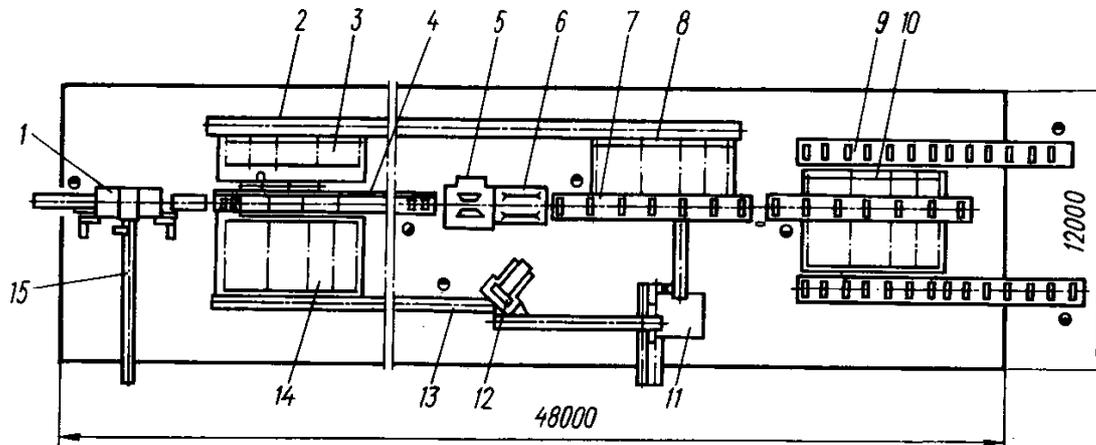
Технологическая схема лесопильного цеха с головным фрезерно-брусующим станком для тонкомерного сырья: 1 – окорочный станок; 2, 13 – ленточные конвейеры; 3, 8, 14 – цепные конвейеры; 4, 5, 7 – фрезерно-брусующий станок с околостаночной механизацией; 6 – делительный модуль; 9 – роликовый конвейер; 10 – реверсивный цепной транспортер; 11 – устройство для сортировки щепы; 12 – рубительная машина; 15 – конвейер для отходов окорки
